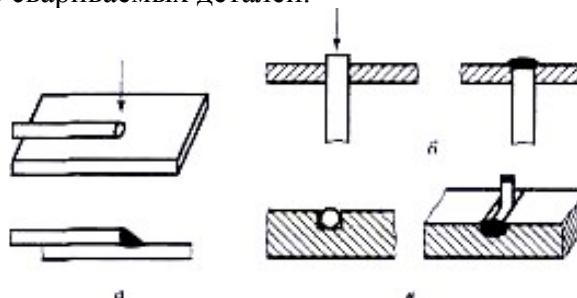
Типы соединений проволоки с массивными деталями:
